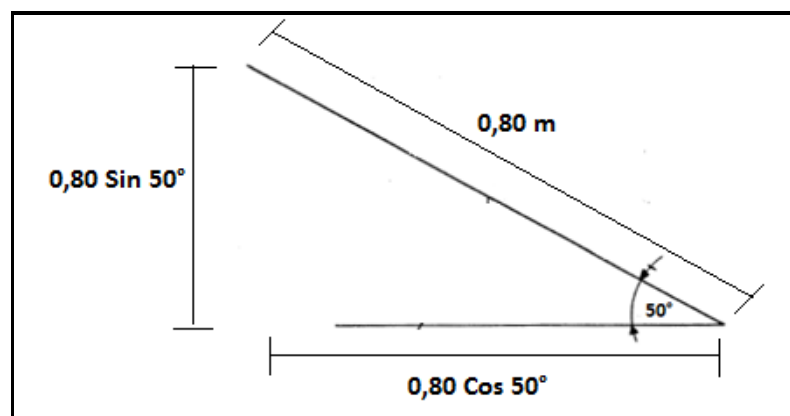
DIMENSIONES DE LA PLACA METÁLICA.
